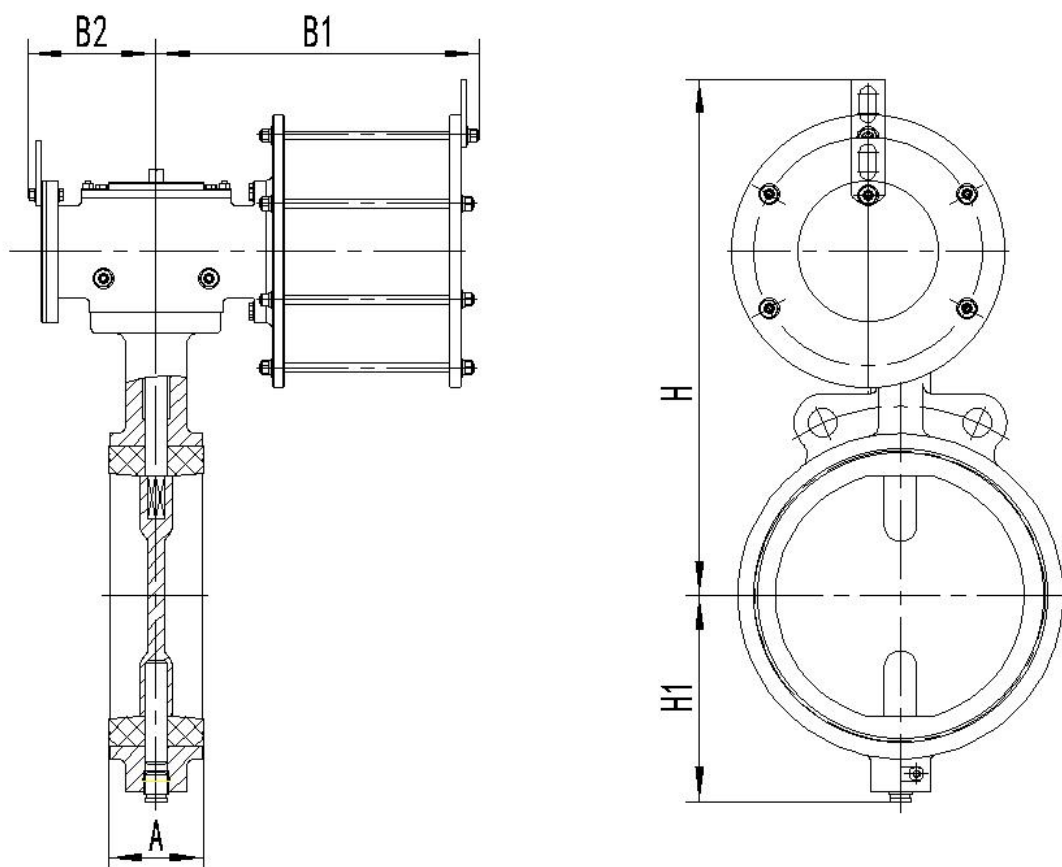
配 HCW18D001~HCW50D005 外形尺寸图
